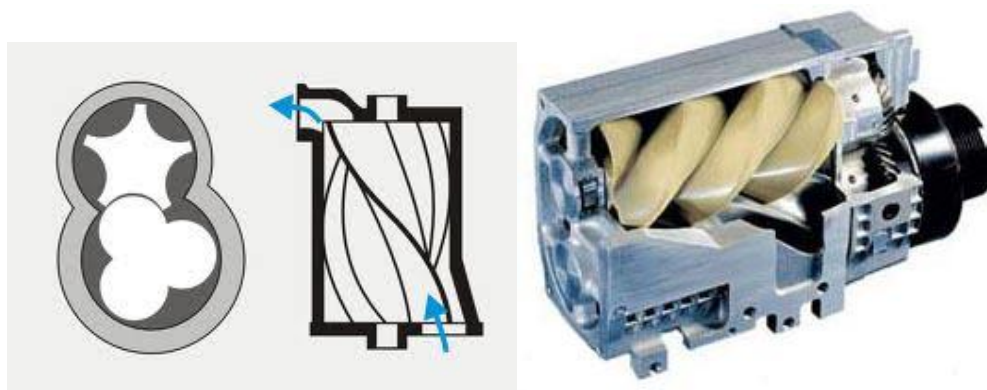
Схема нагнетателя конструкции Лисхольм
